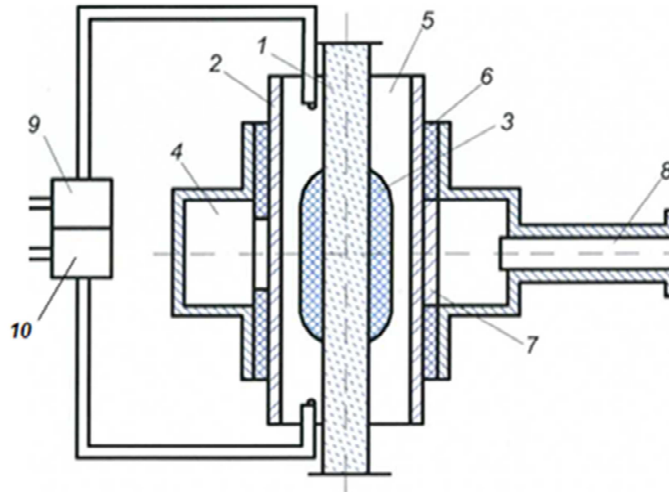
Схема процесса осаждения фторсиликатной и защитной оксинитридной оболочек на боковую поверхность кварцевого стержня (заготовки):
